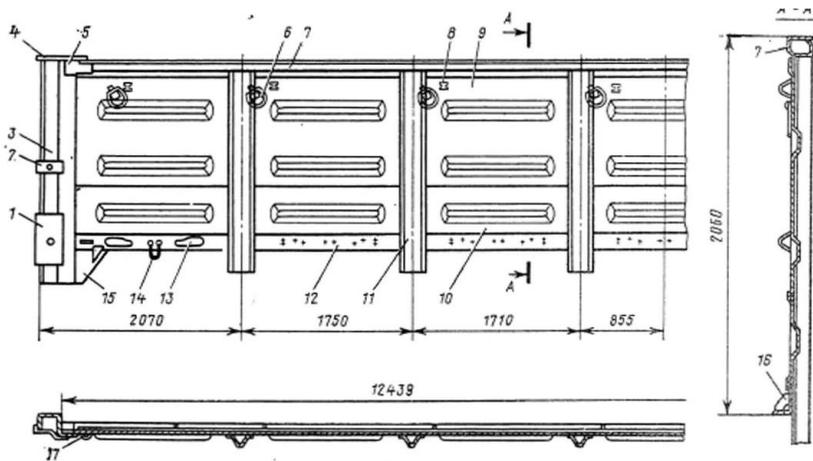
Боковая стена универсального четырехосного полувагона
